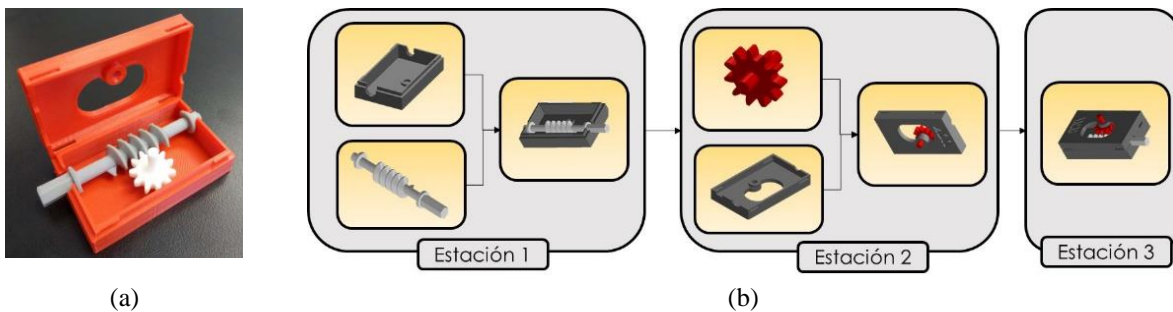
(a) Dispositivo didáctico y (b) secuencia de ensamblaje de componentes.
